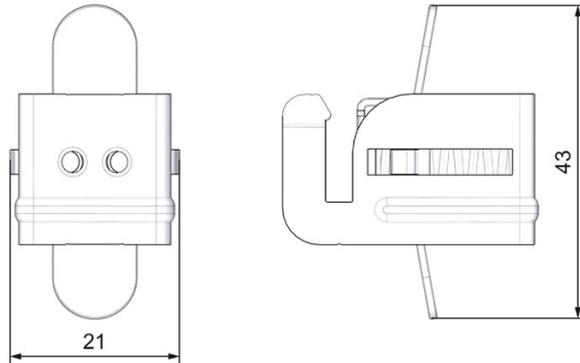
Croquis acotado de la abrazadera de pantalla para módulos de 25 mm
